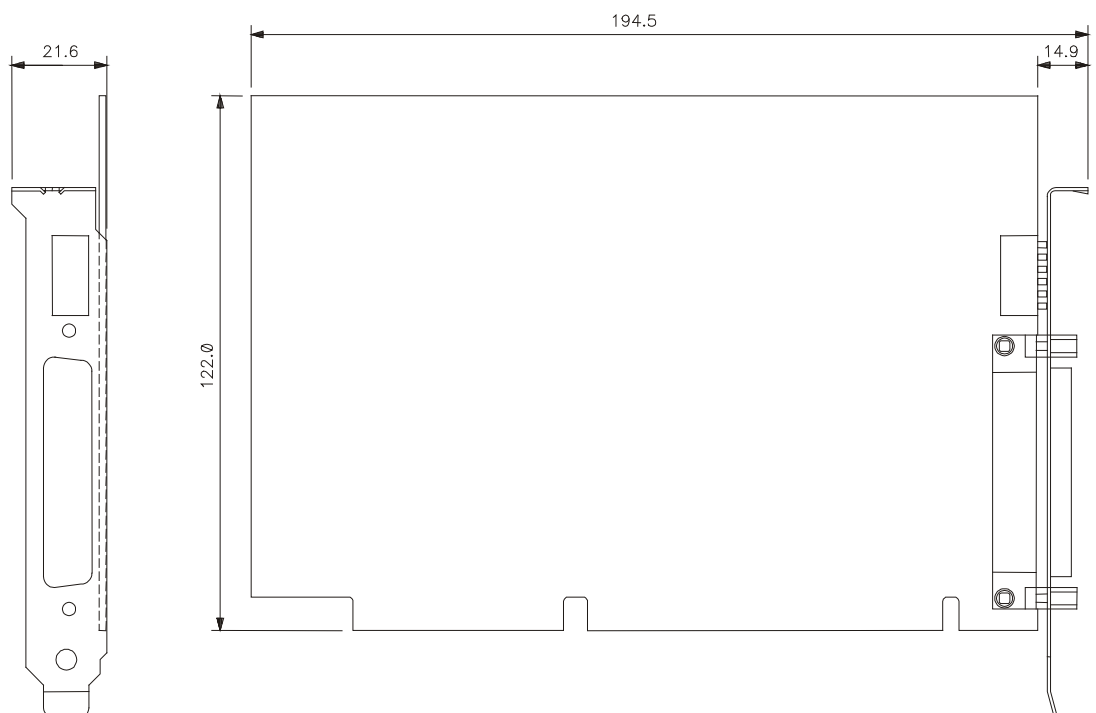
Dimensões Físicas do Cartão PCI302 V1.2x (mm)
